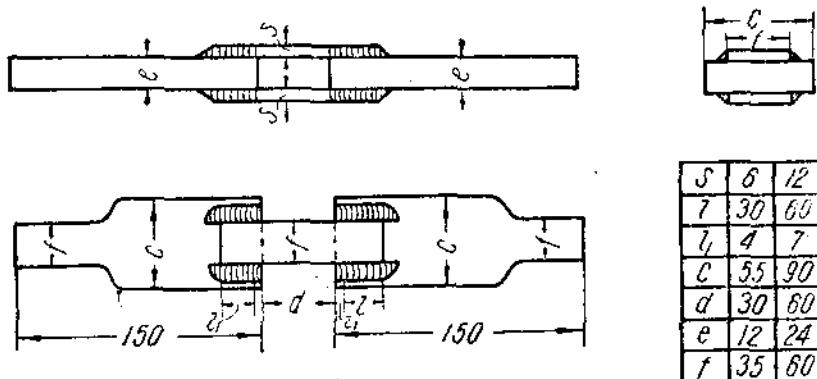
Образцы для сварки боковым валиковым швом (тип б).
